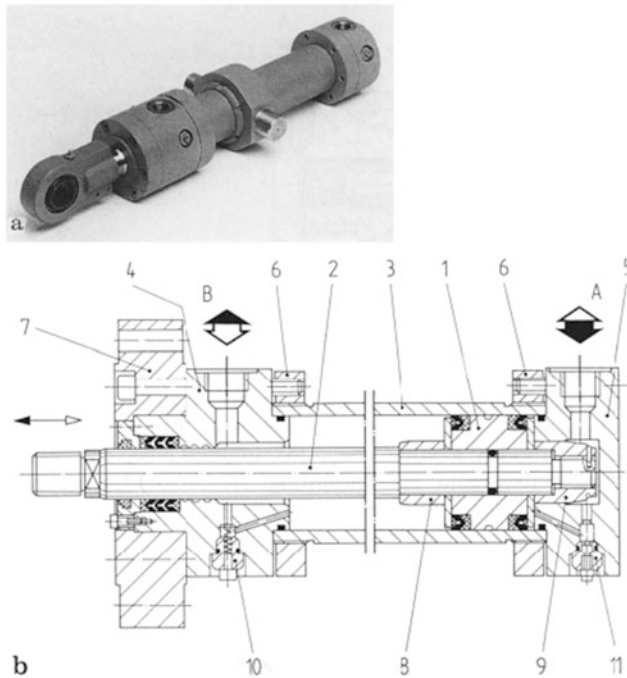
Differenzialzylinder in Rundbauform (DIN ISO 6022; CD 251, schwere Ausführung, Bosch Rexroth). a Mit Drehzapfenbefestigung; b mit Kopfflanschbefestigung. 1 Kolben mit Lippensatz-(Dachmanschetten-Dichtsatz-) Kolbendichtung, 2 Kolbenstange, 3 Zylinderrohr, 4 Zylinderkopf mit Stangenführung direkt im Kopf, Mehrfach-Lippensatz-Stangendichtung, Abstreifer, 5 Zylinderboden, 6 Flansch am Zylinderrohr, 7 Kopfflansch, 8 Dämpferkolben mit Buchse, 9 Dämpferzapfen mit Buchse, 10 Rückschlag-Einbauventil mit Entlüftung, 11 Drossel-Einbauventil einstellbar
